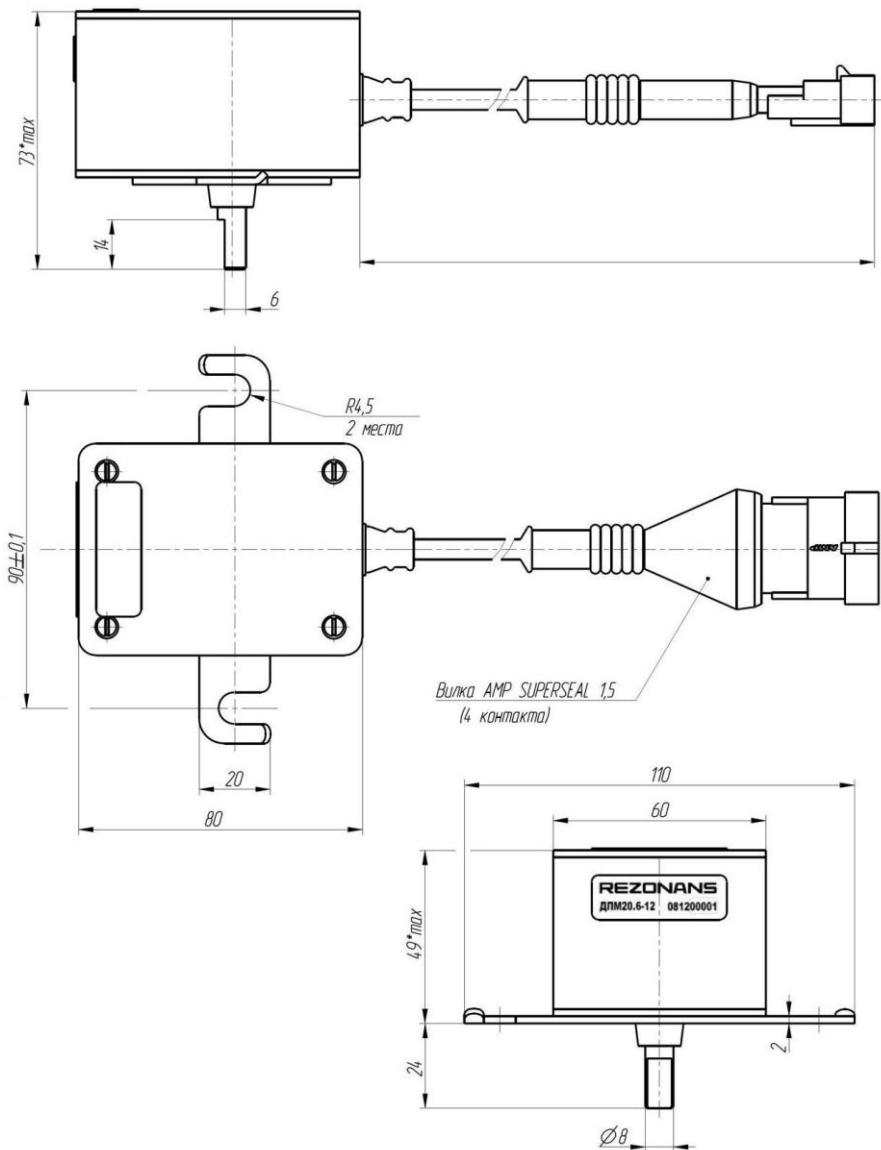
Габаритные и присоединительные размеры ДПМ20.6-12
